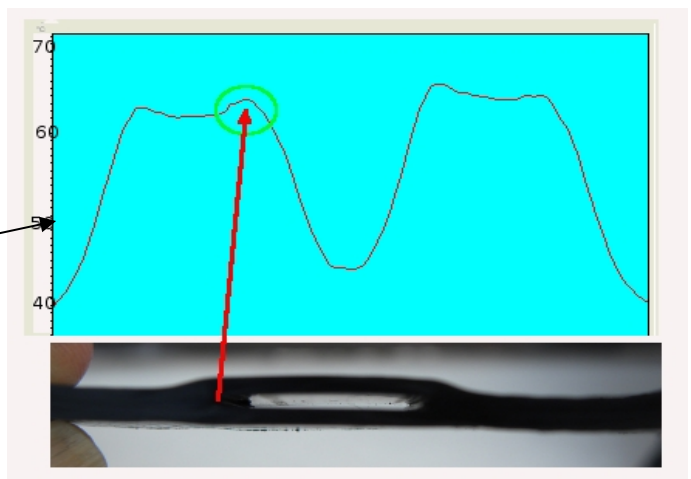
Vue du profil P1 de température obtenu et de la découpe de la soudure à ce niveau
